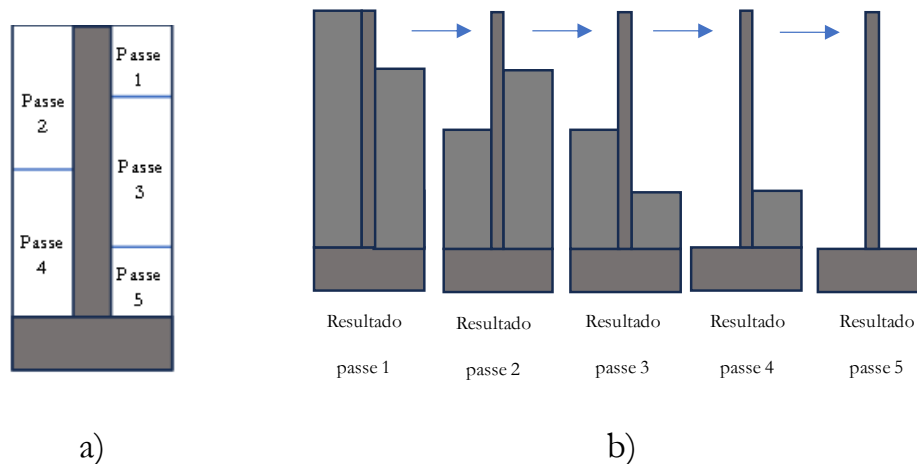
Estratégia de maquinagem adotada para paredes finas: a) passes sucessivos; b) remoção de material.
